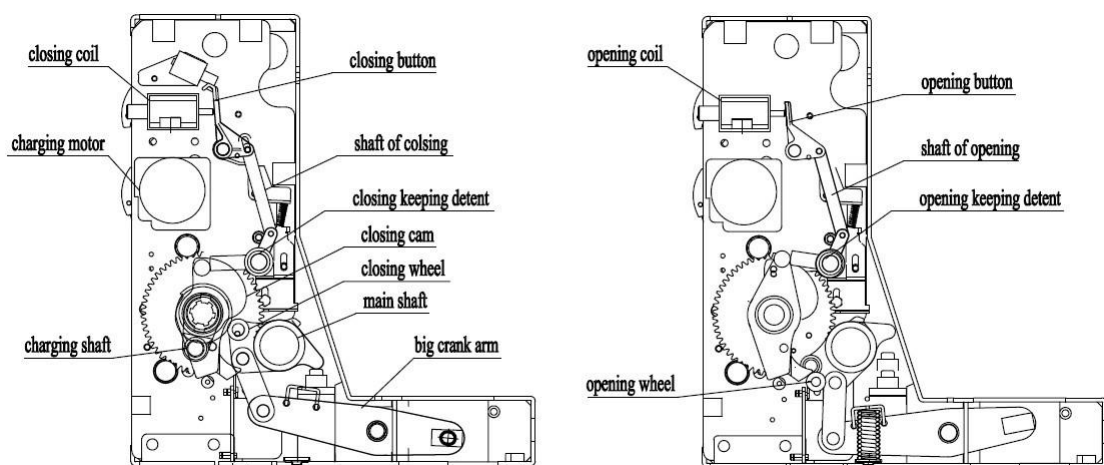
Конструкция привода выключателя. Взвод пружины (перевод в положение «charged»)
